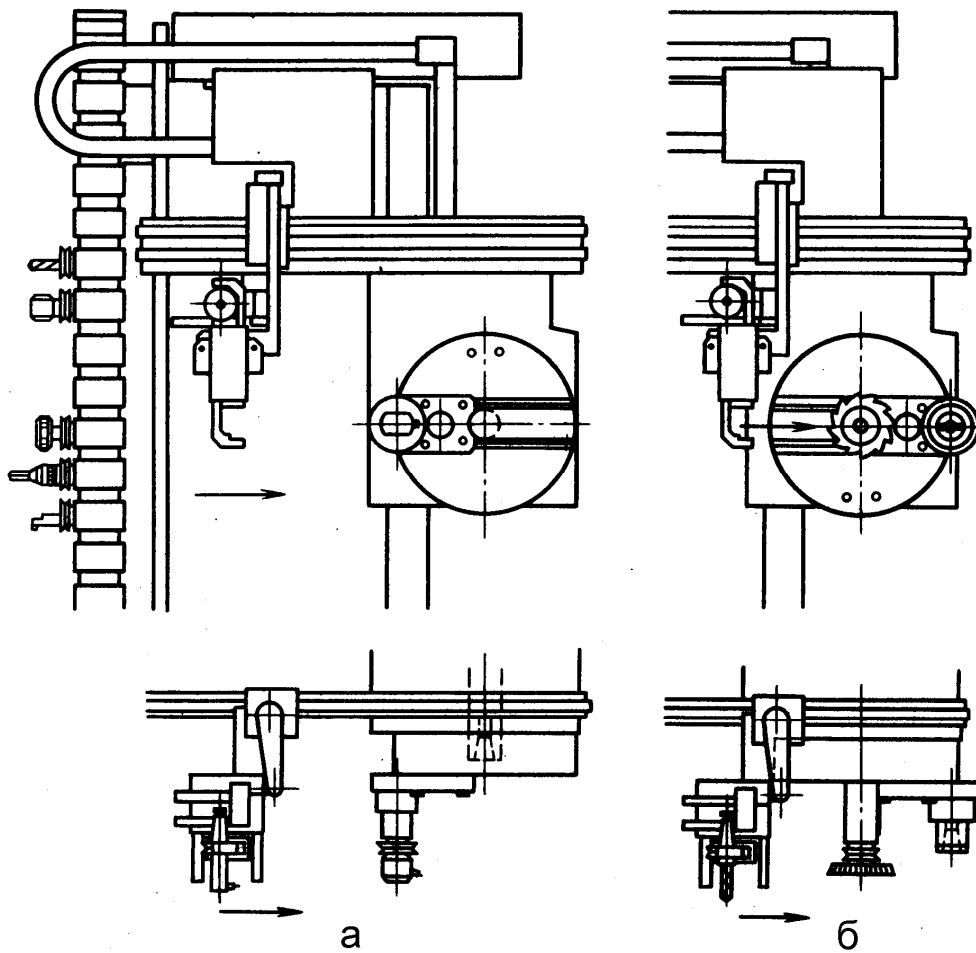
Механізм автоматичної заміни інструменту фірми «Пегар»:
